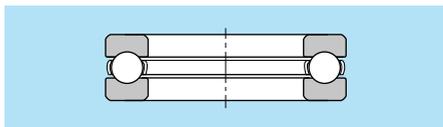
Einseitig wirkende Axialkugellager (Beispiel mit Stahlblechkäfig)
